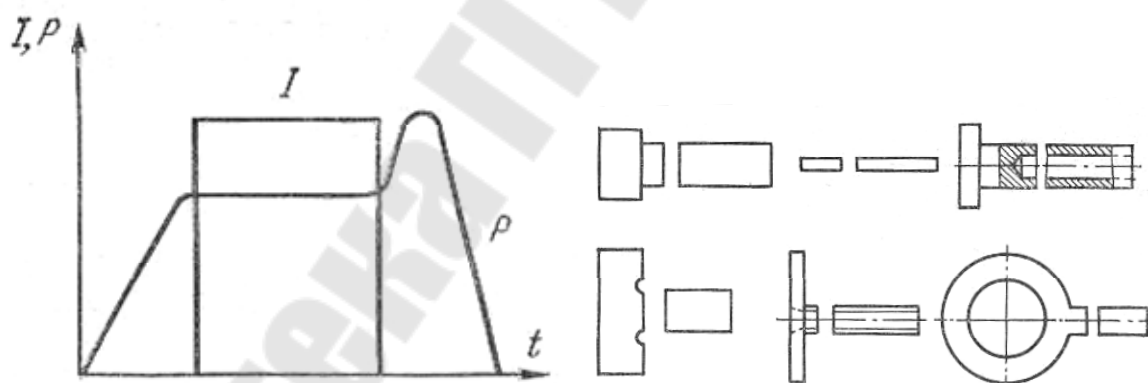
Циклограмма стыковой сварки сопротивлением и типы сварных соединений.
